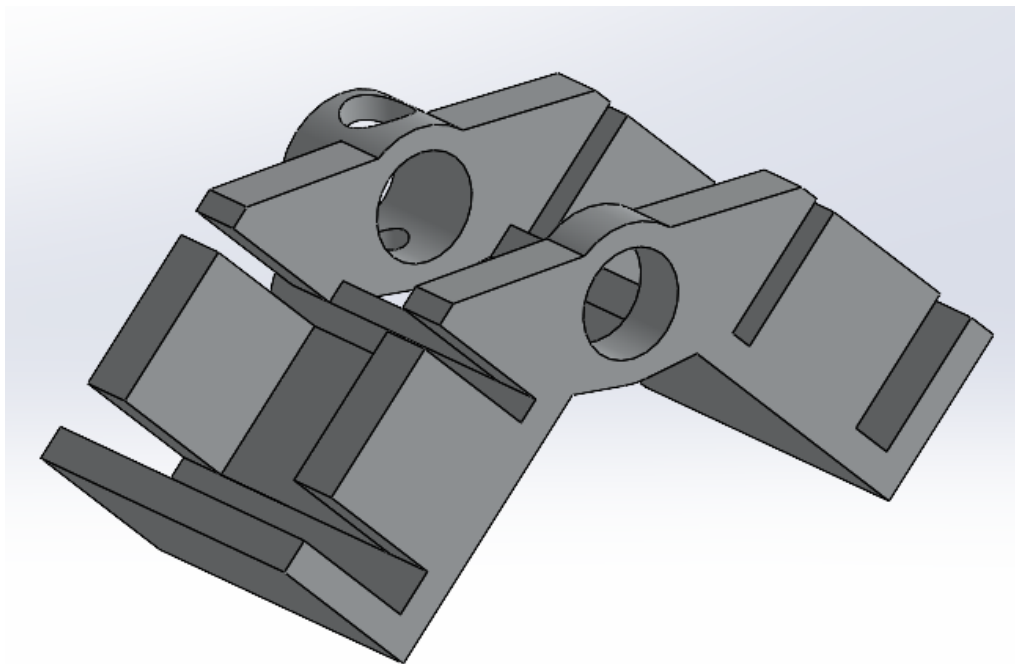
Ізометричний вигляд посадочного тримача серводвигунів
